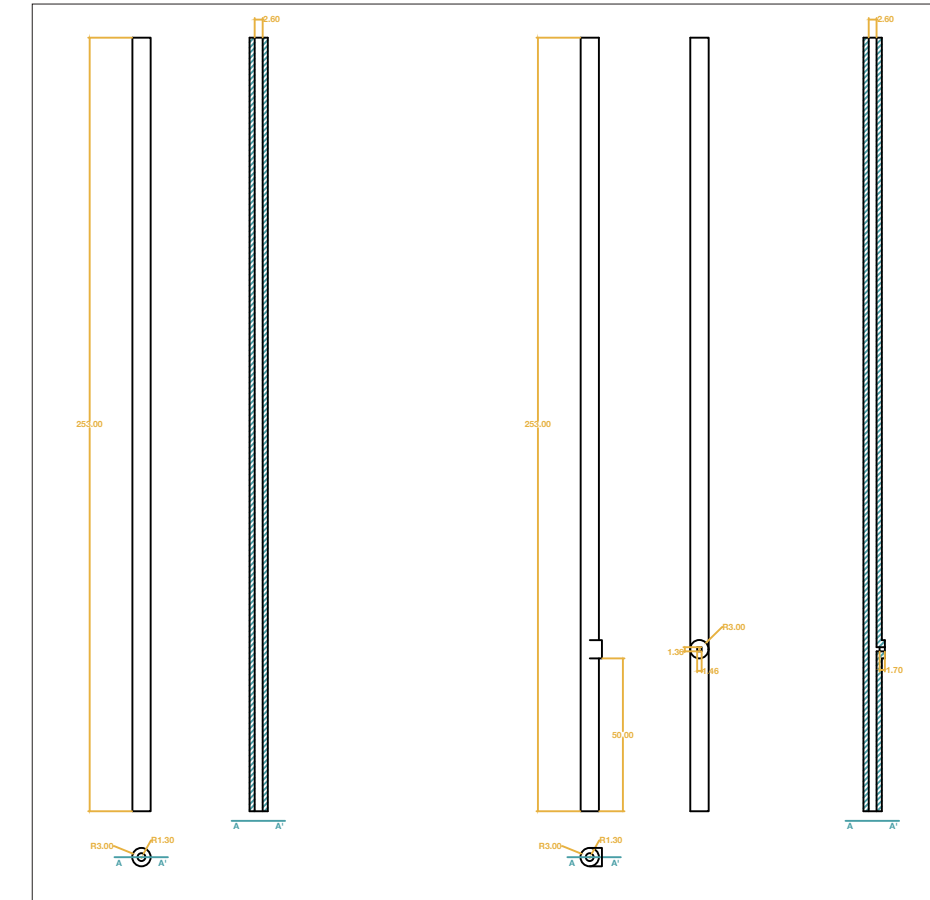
Planta, alzado y sección de la Columna 253 A y de la Columna 253 B.
